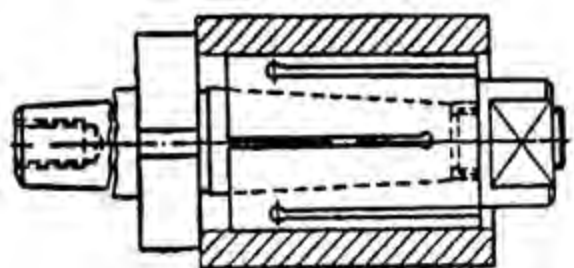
Установка заготовок на розтискній цанговій оправці
